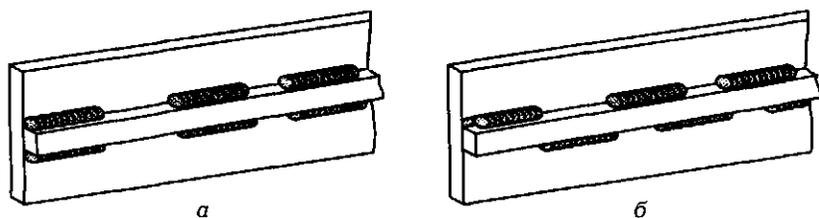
Цепной прерывистый (а) и шахматный прерывистый (б) швы
